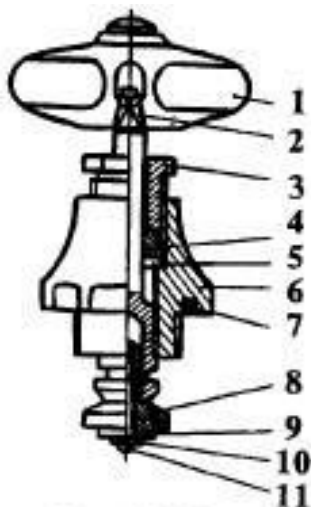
Устройство вентильной головки: 1 — маховичок; 2 — шпиндель; 3 — гайка; 4 — сальник; 5 — шайба; 6 — корпус; 7 — прокладка; 8 — клапан; 9 — прокладка; 10 — шайба; 11 — винт
